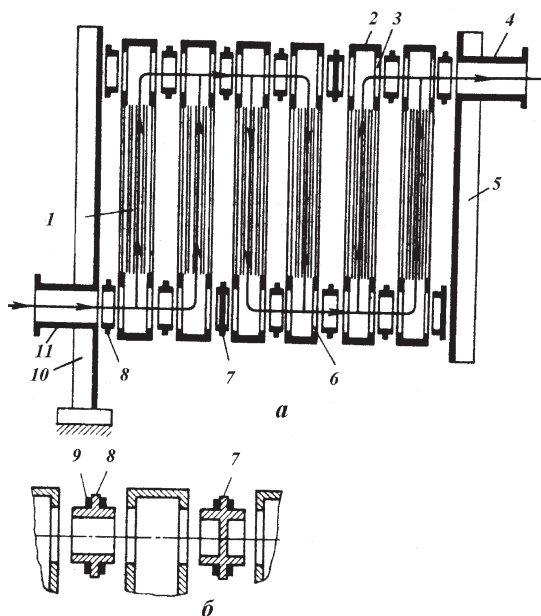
Блочный сварной пластинчатый теплообменник: а — общий вид; б — вид проходных втулок; 1, 2 — унифицированные сварные блоки; 3 — верхние отверстия, 4 — патрубок выхода рабочей среды; 5 — подвижная плита; 6 — нижние отверстия; 7 — глухие втулки; 8 — проходные втулки; 9 — кольцевые прокладки; 10 — неподвижные плиты; 11 — патрубок входа рабочей среды
